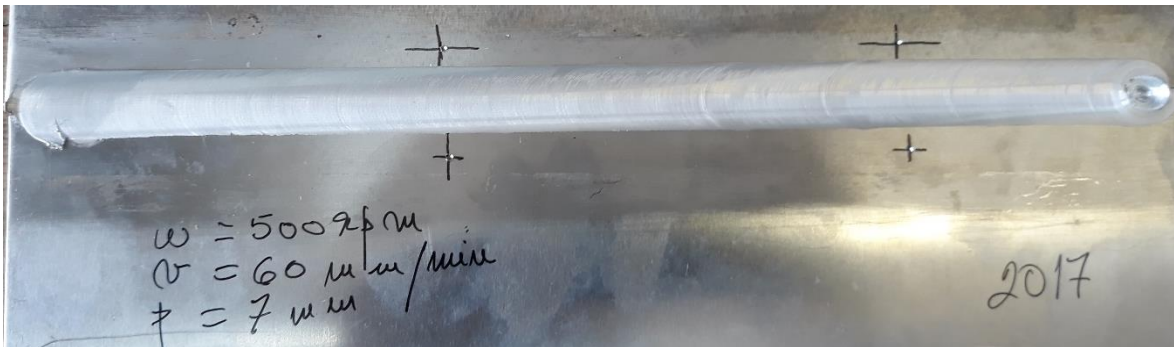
Estado superficial da soldadura 562BRP-2
